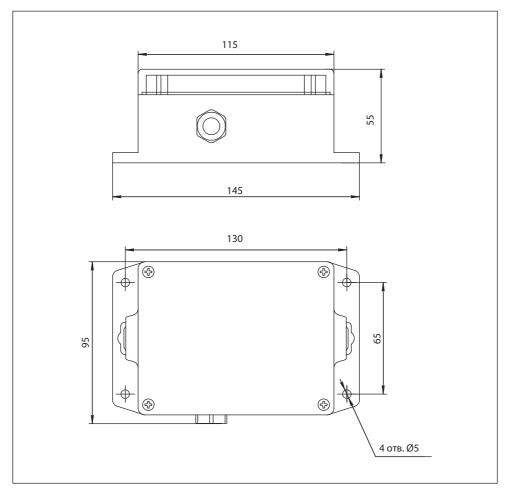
Габаритный чертеж газоанализатора "Сенсон-СВ-5024"
